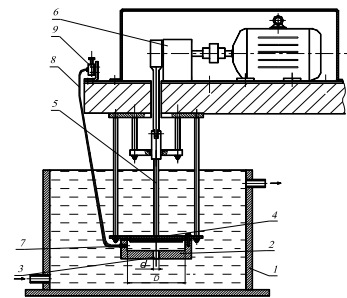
Конструктивна схема кавітаційного пристрою для обробки води: 1 – ємкість; 2 – корпус; 3 – отвір; 4 – мембрана; 5 – шток; 6 – ексцентриковий вібратор; 7 – штуцер; 8 – шланг; 9 – повітряний дросель
